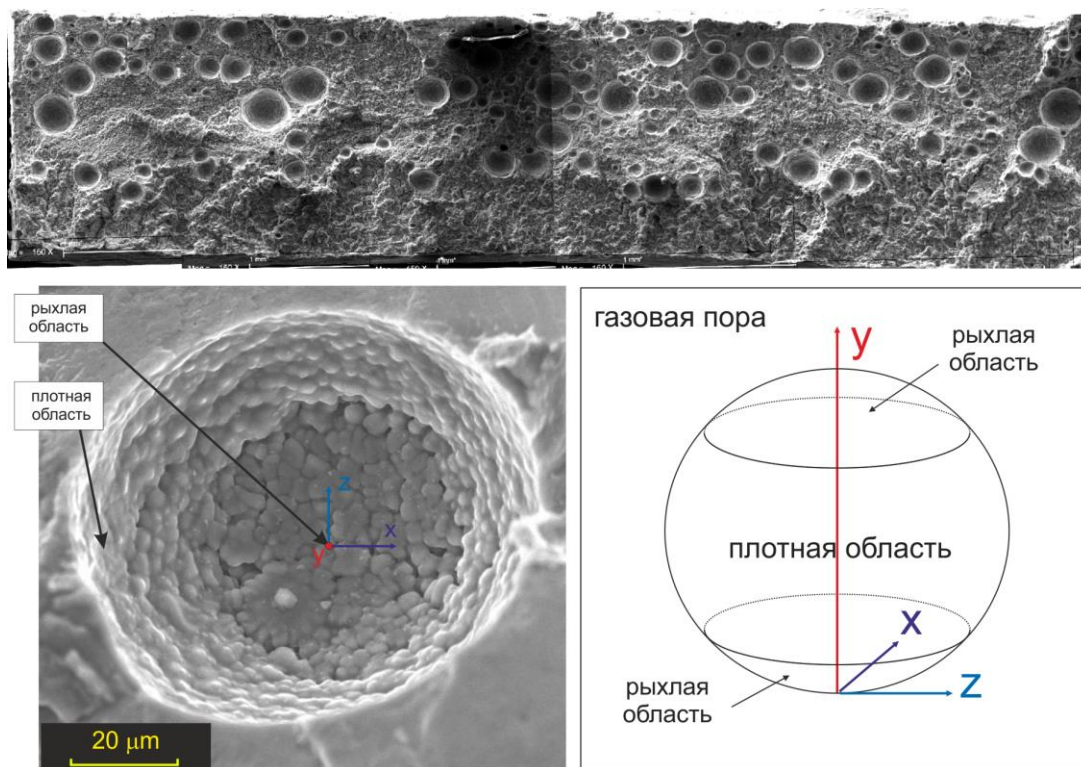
Газовые поры в лазерном сварном шве сплава 1420.
